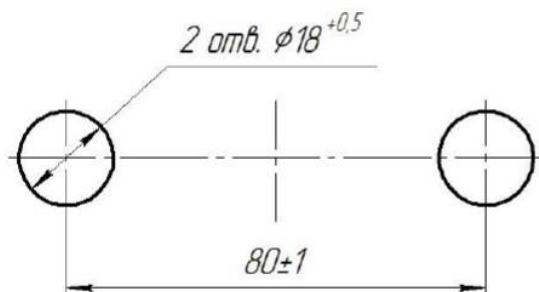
Эскиз отверстий, выполняемых в опоре ЛЭП для подвешивания узла крепления устройств I-TOR (E-TOR)
